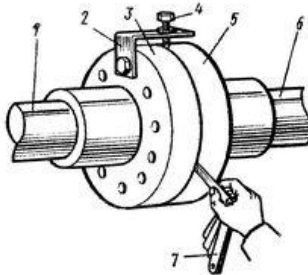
Центровка валів методом обходу одною точкою
